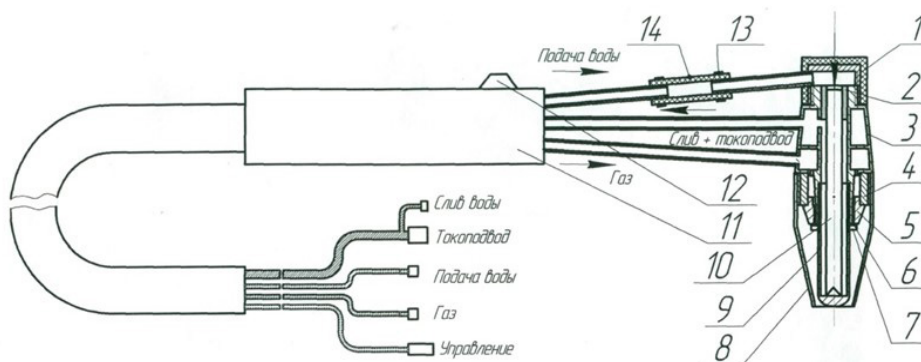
Схема соединений плазмобразующего газа (аргона), подачи и слива охлаждающей воды, подвода тока и управления технологического плазмотрона: 1 – гайка; 2, 6 – уплотненная прокладка; 3 – корпус; 4 – резьбовая втулка; 5 – рассекатель; 7 – гайка для электрода; 8 – керамическое сопло; 9 – электрод; 10 – трубка; 11 – ручка; 12 – кнопка; 13 – хомут; 14 – соединительный рукав.
